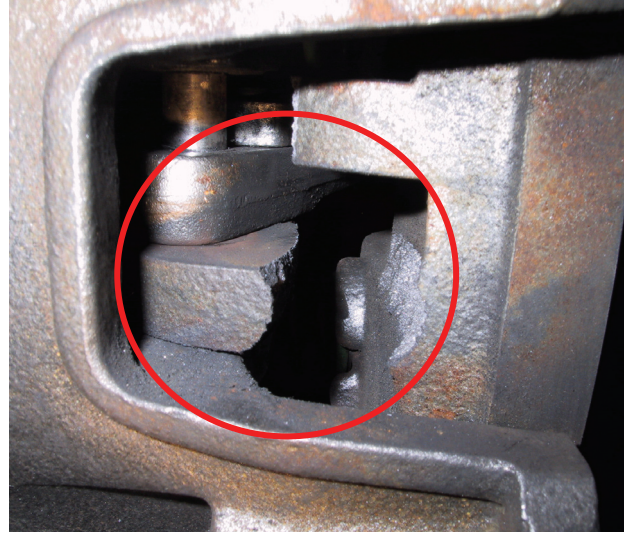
Painelevyn ohjausnokat ovat murtuneet
